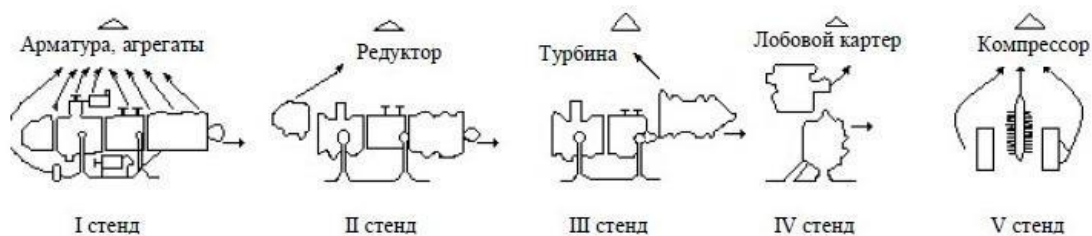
Схема поточной линии разборки авиадвигателя
